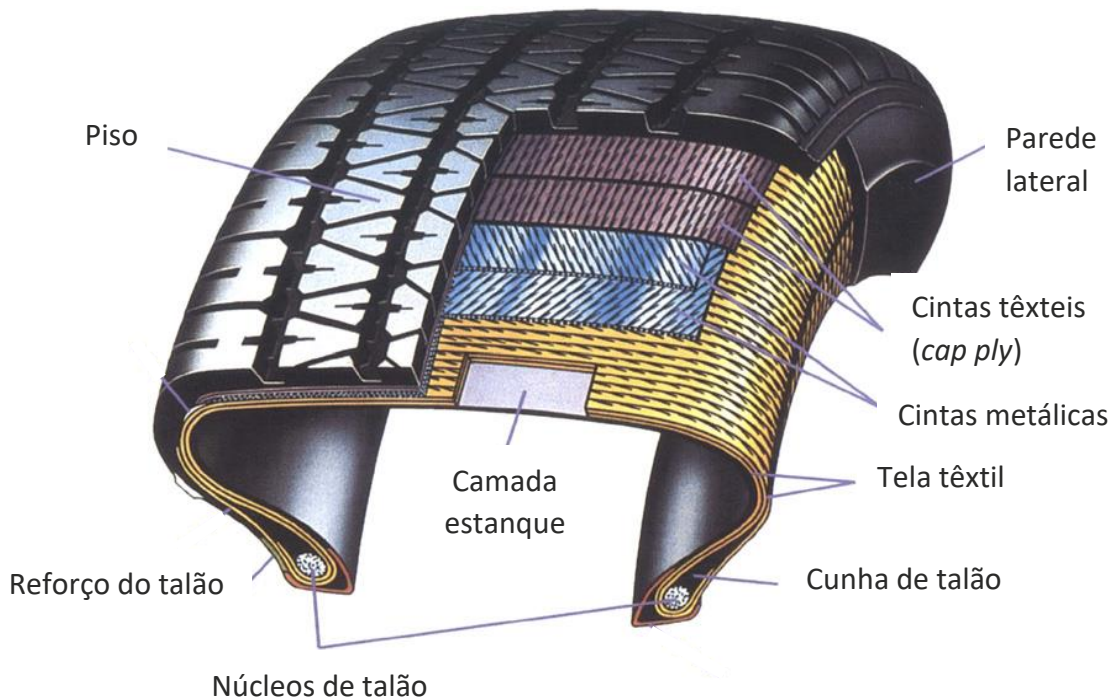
Secção de corte de um pneu radial de um automóvel de passageiros [4].
